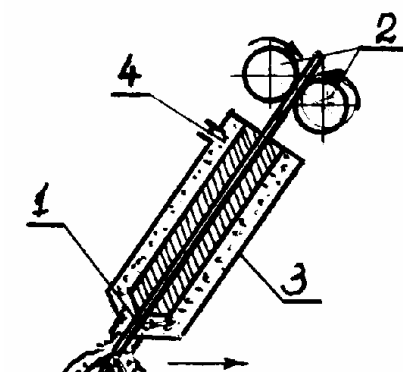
Сварочная головка, применяемая при автоматической сварке
